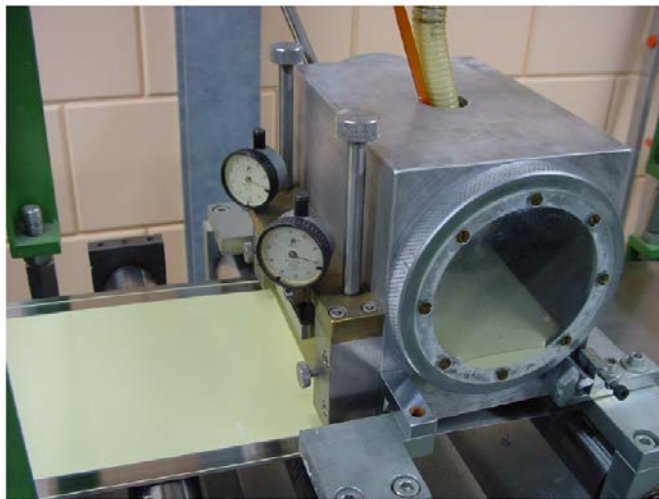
Gießwerkzeug mit Doctor Blade und Füllstandsfenster
